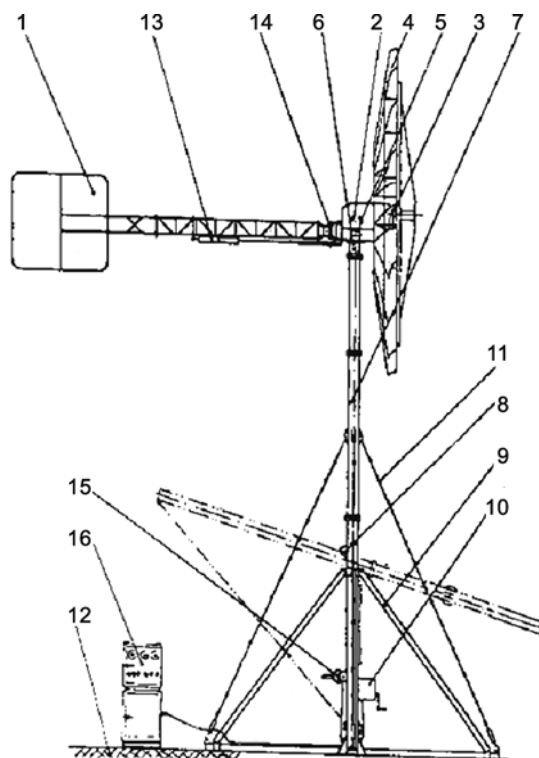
Внешний вид и принципиальная схема ветроустановки ВЭУ-5-4: 1 – киль; 2 – платформа поворотная; 3 – ветроколесо; 4 – лопасти; 5 – балка боковая со щитом; 6 – опорный узел; 7 – башня; 8 – шарнир; 9 – основание; 10 – лебедка; 11 – растяжка; 12 – фундамент; 13 – механизм останова; 14 – шарнир; 15 – привод; 16 – электрооборудование (кроме установленного в поворотной платформе)
